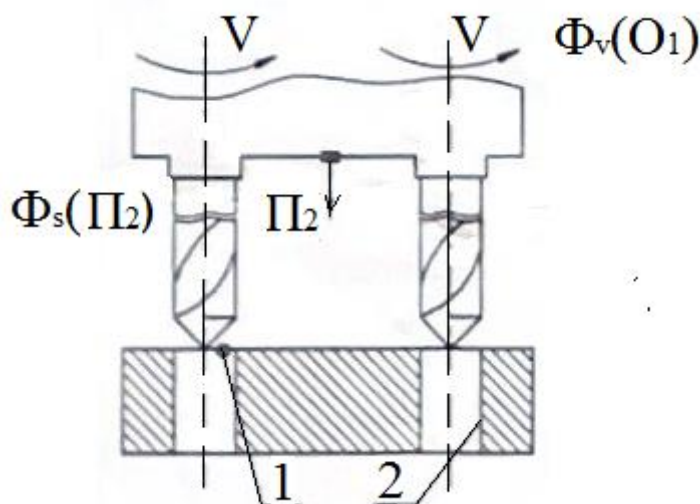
Схема рухів формоутворення при свердлінні багатошпindelного верстату
